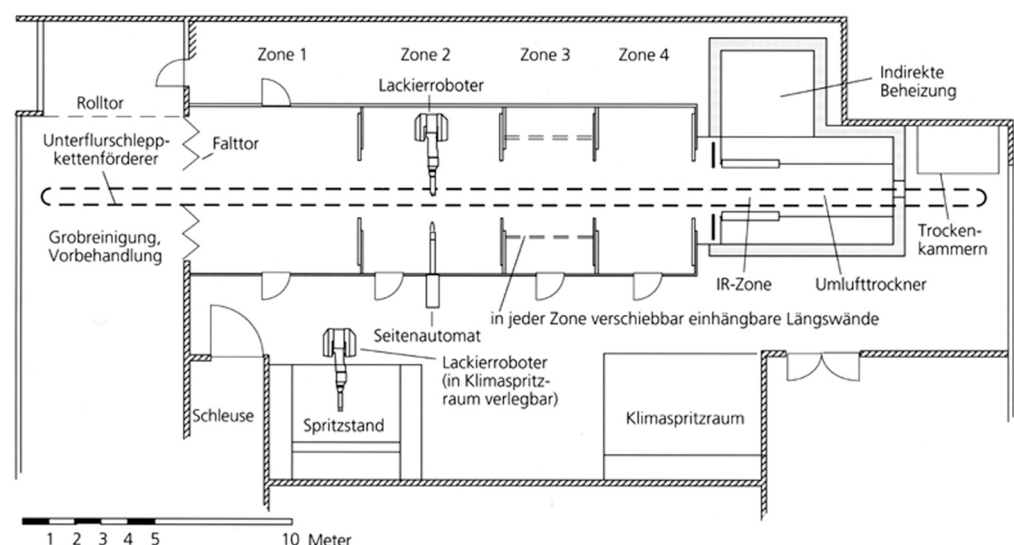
Skizze Lackiertechnikum im Fraunhofer IPA
